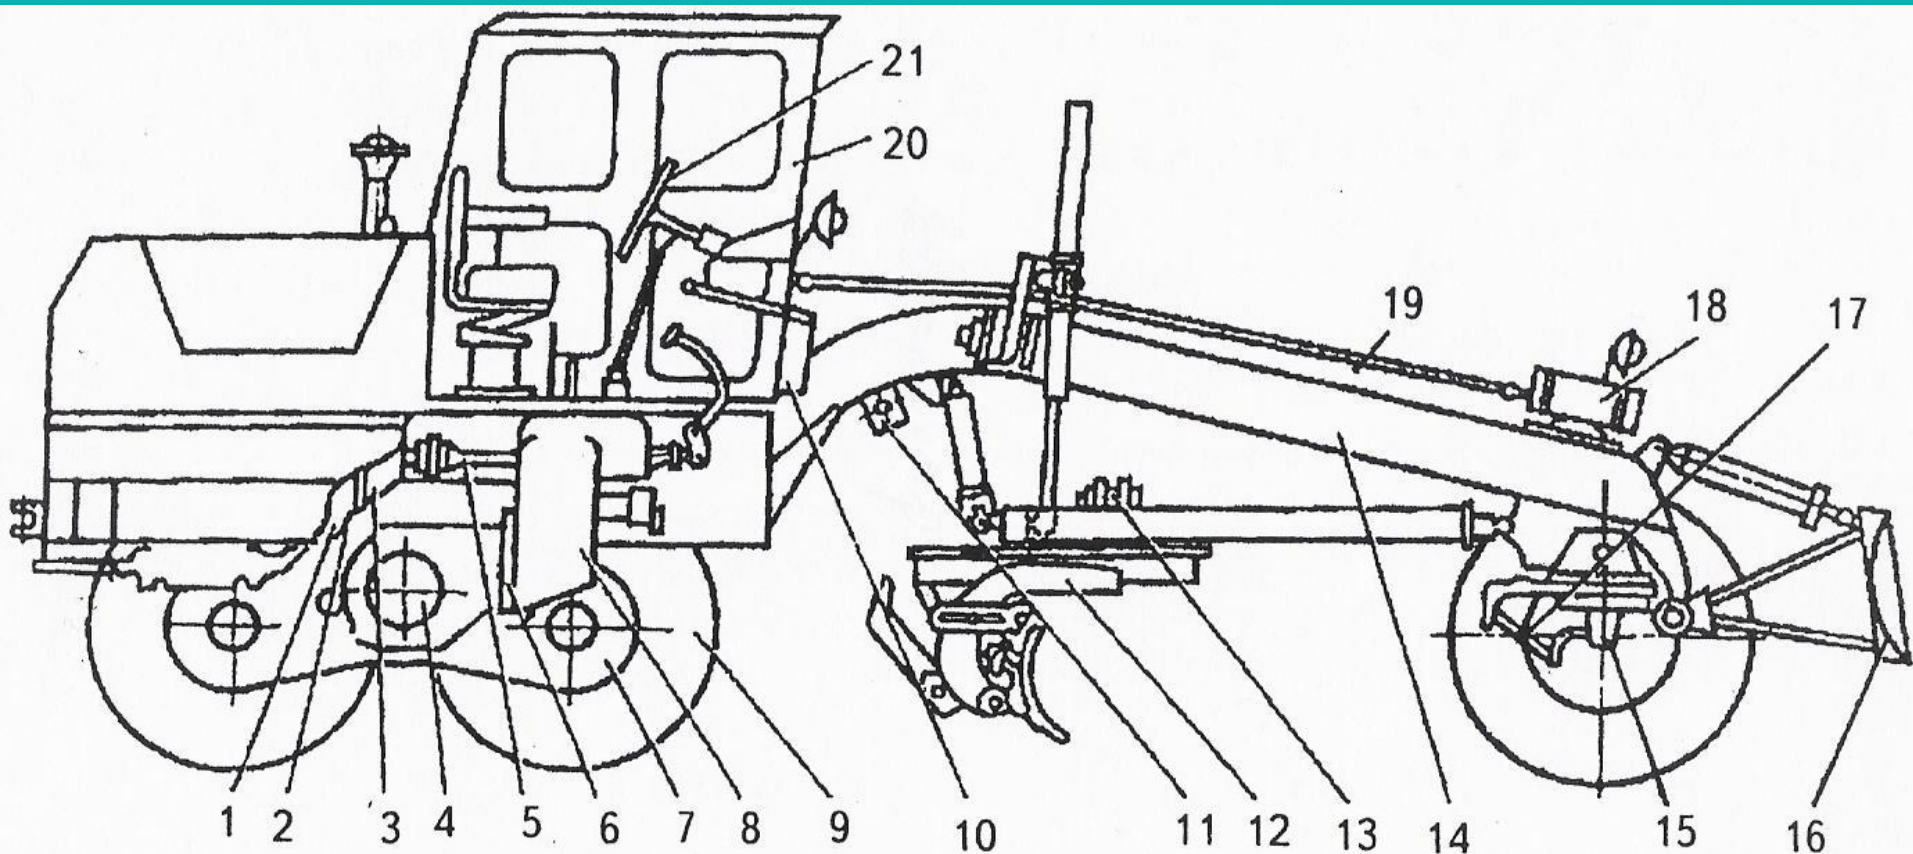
Автогрейдер: 1 – двигатель; 2 – коробка отбора мощности; 3 – муфта сцепления; 4 – задний мост; 5, 6 – соединительные валы; 7 – баланси́р; 8 – коробка передач; 9 – ходовые колеса; 10 – гидравлика; 11 – распределитель; 12 – рабочий орган; 13 – система автоматического устройства; 14 – рама; 16 – бульдозерный отвал; 17 – механизм поворота колес; 18 – рулевой механизм; 19 – карданная передача; 20 – кабина; 21 – рулевое колесо
